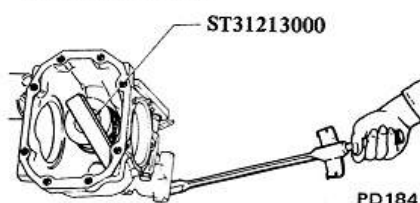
Serrage de l'écrou du pignon d'attaque
